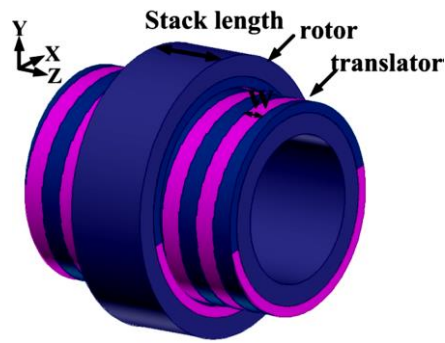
Engrenage magnétique trans-rotatif [PAK12]
